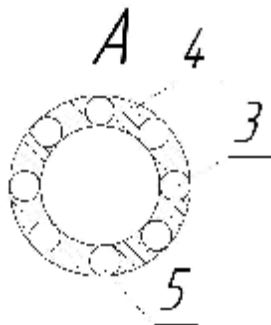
Вид снизу зубчатой коронки 4 по направлению А
